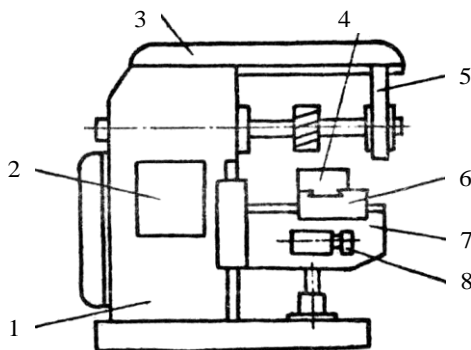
Общий вид горизонтально-фрезерного станка:
